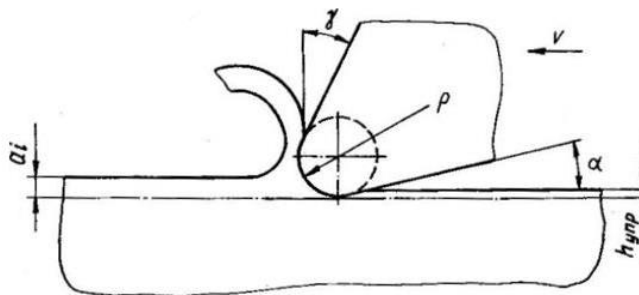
Схема врзання зуба фрези при зубофрезеруванні зубчастих коліс
